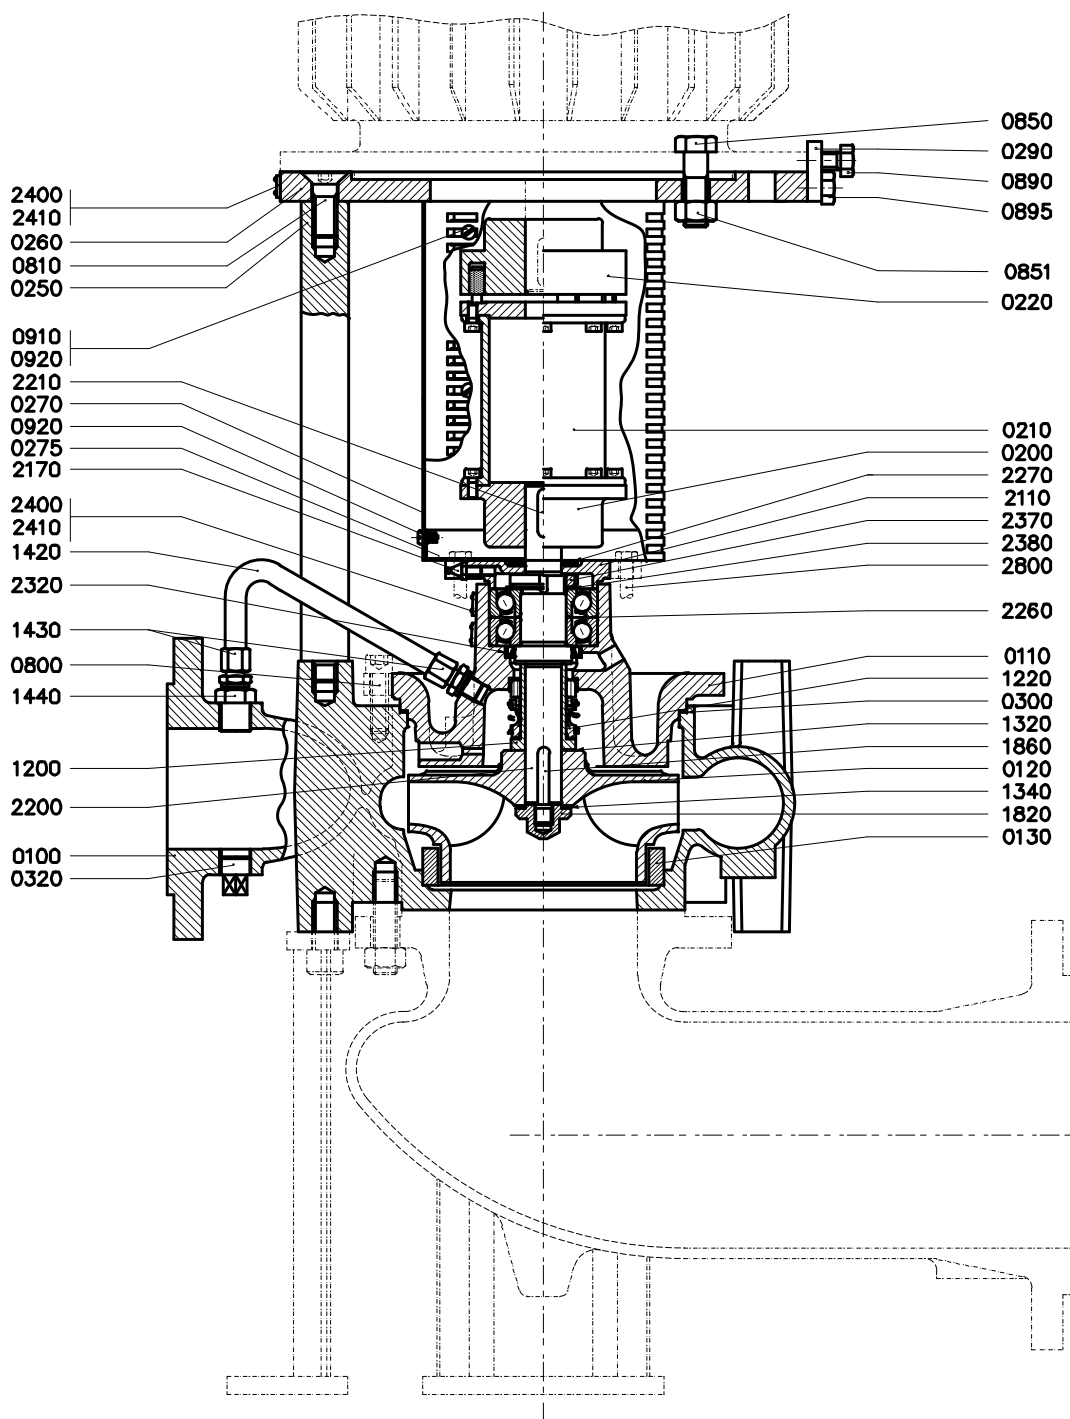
Чертеж в разрезе ..-160/..-200/..-250.
